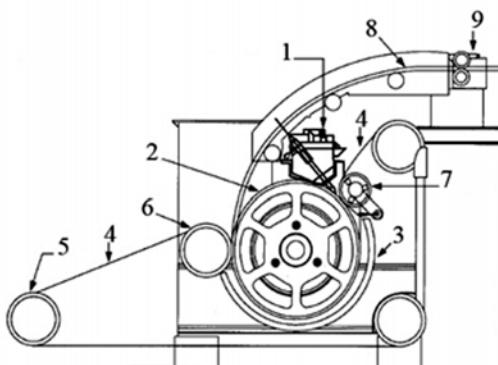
Схема розливання на колесо. 1 – проміжний ківш; 2 – розливальне колесо; 3 – система водяного охолодження; 4 – сталева стрічка; 5 – натяжний ролик; 6 – направляючий ролик; 7 – притискний ролик; 8 – заготовка; 9 – прокатна кліть.
